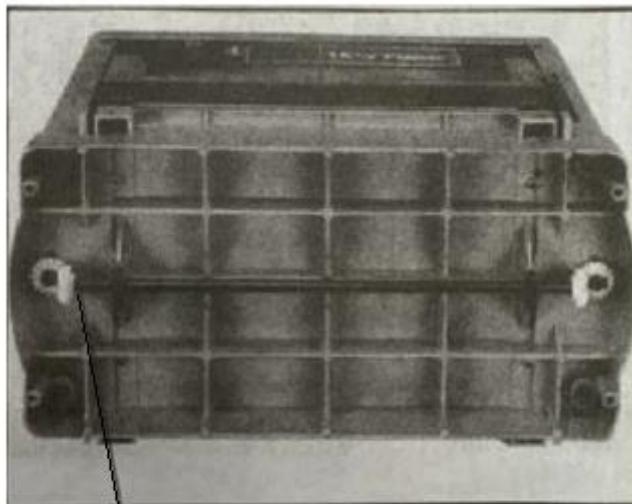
Регулировка параллельности фрезы и рабочего стола
